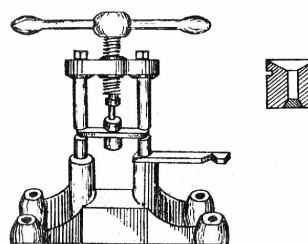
Пресс и матрица для изготовления угольных брикетов
